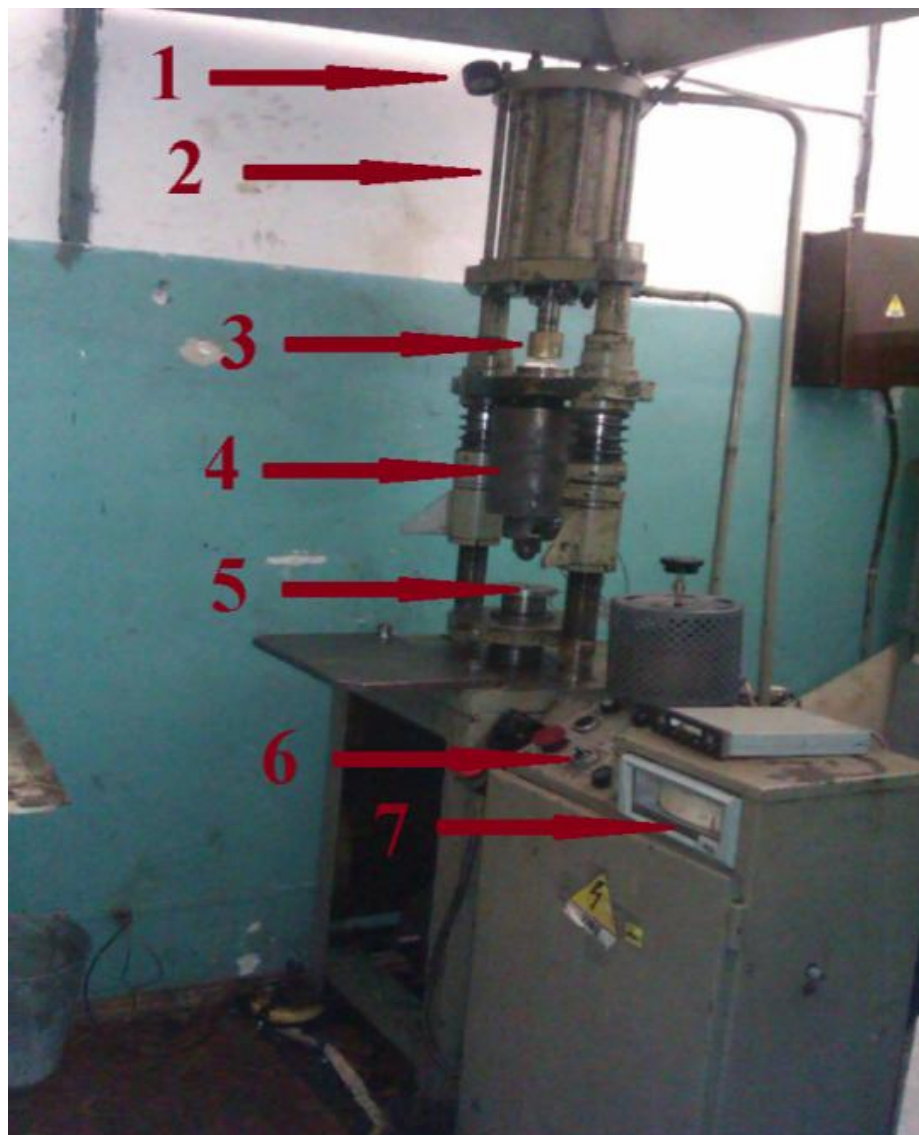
Ливарна машина ручного типу ПЛ-32
